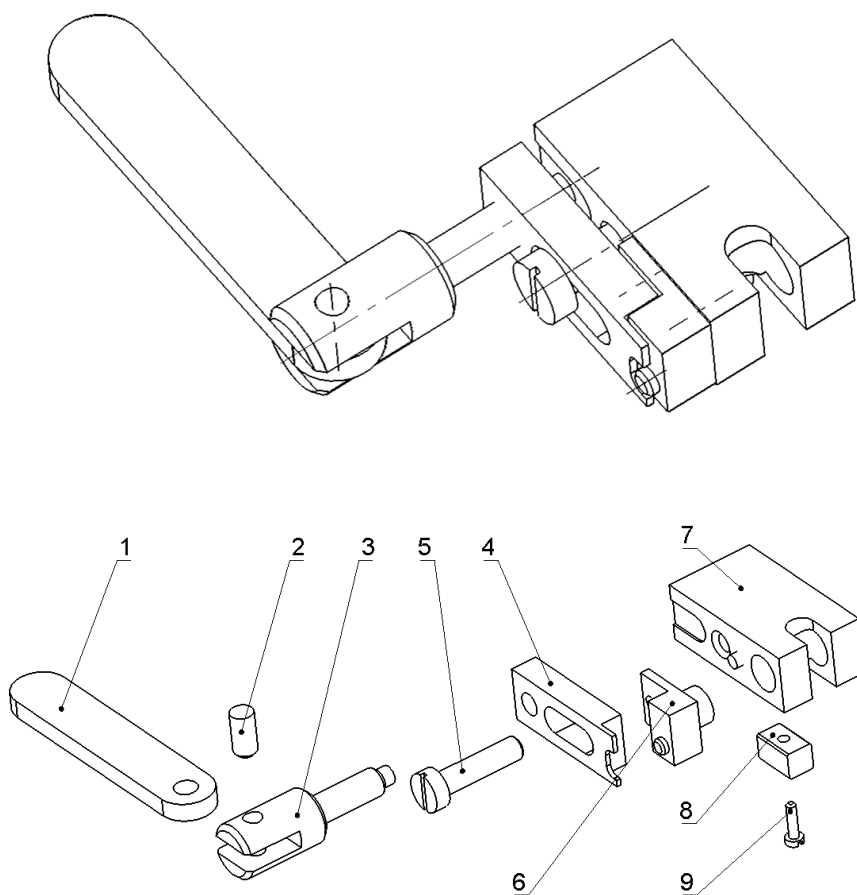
Приспособление для базирования и закрепления заготовки
